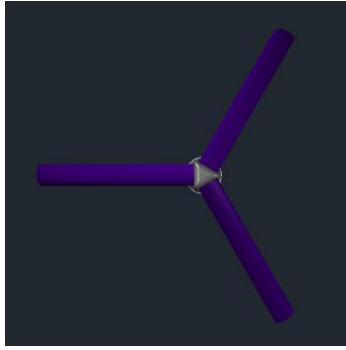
Vista planta de modelo de turbina en AutoCAD (AutoCAD, 2019)
